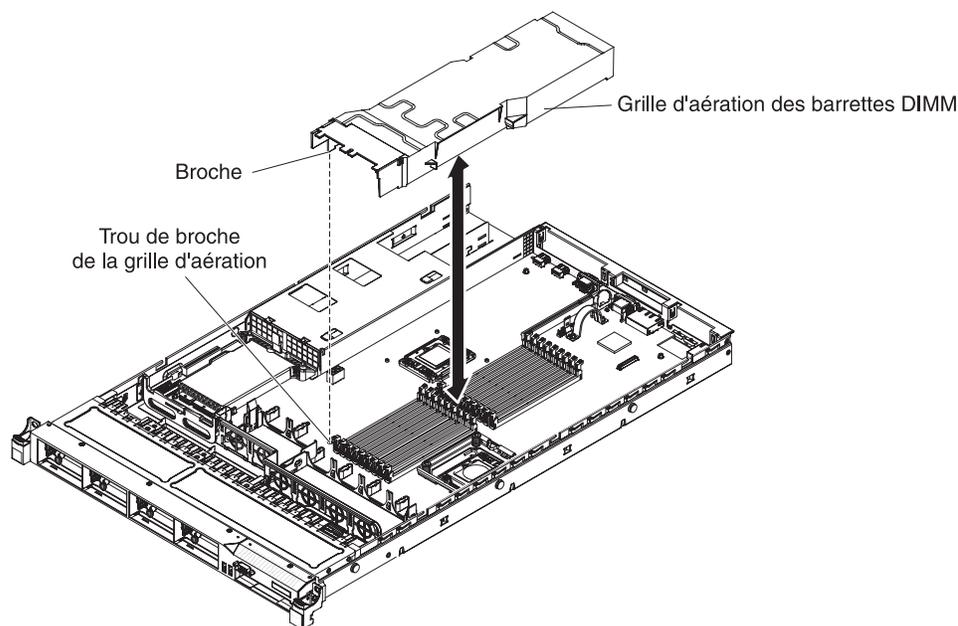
Retrait de la grille d'aération des barrettes DIMM
